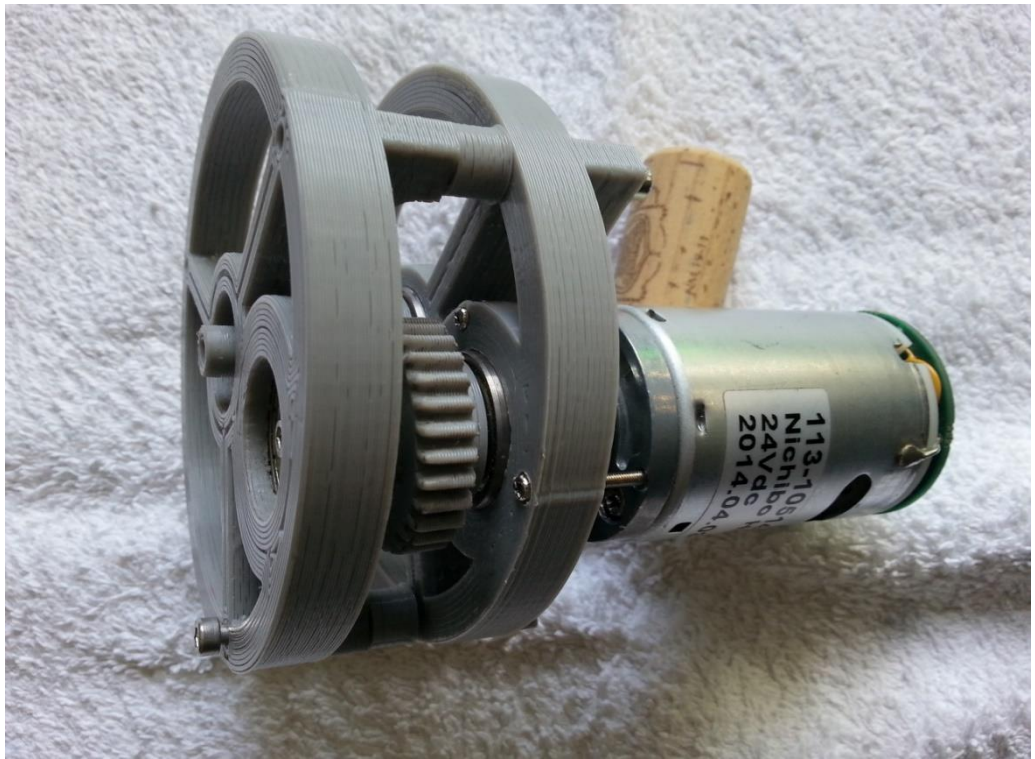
Motor y Sistema de engranaje montado. Fuente Propia.
